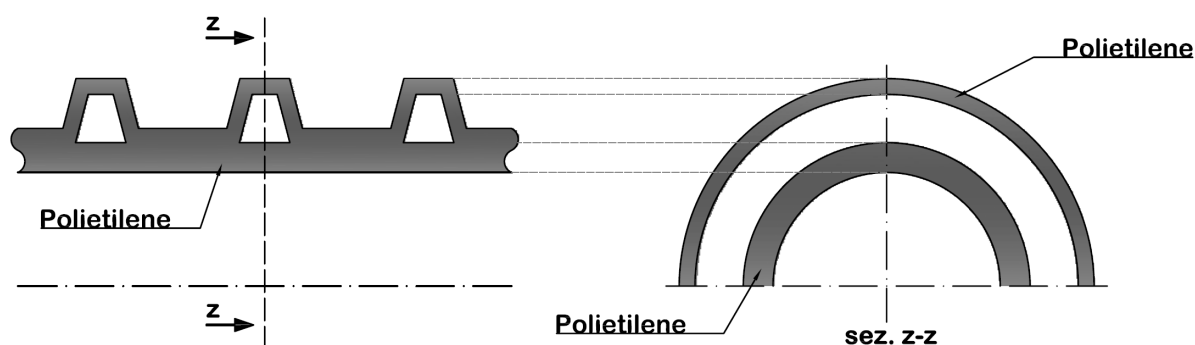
Sezione di una tubazione corrugata a doppia parete (tipo B secondo EN 13476-3:2008).
